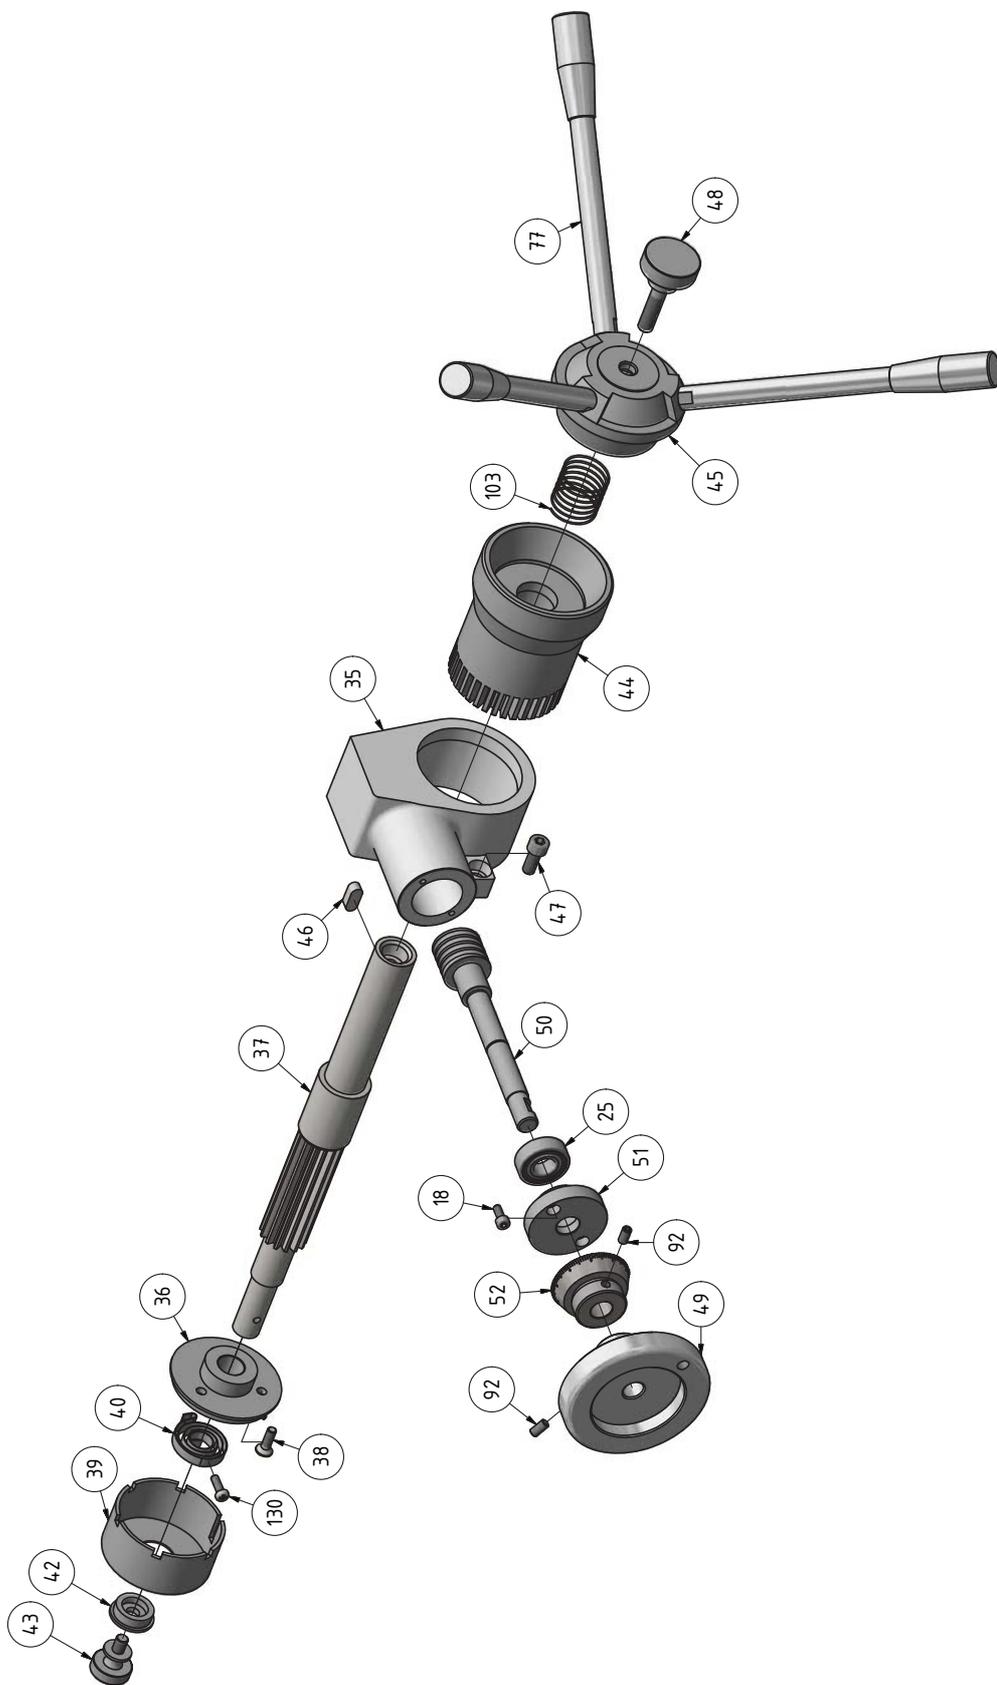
Fräskopf 5 von 6 - Milling head 5 von 6
